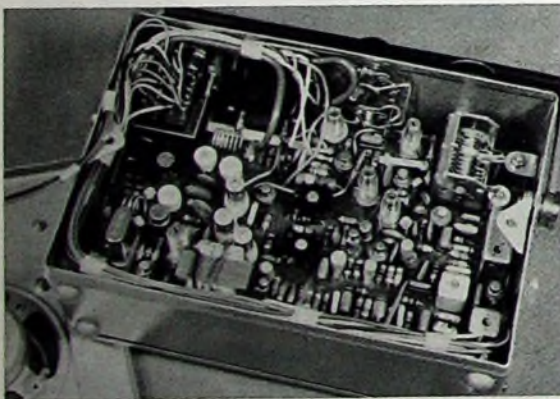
Bestückungsseite der Platine bei abgenommener Frontplatte
